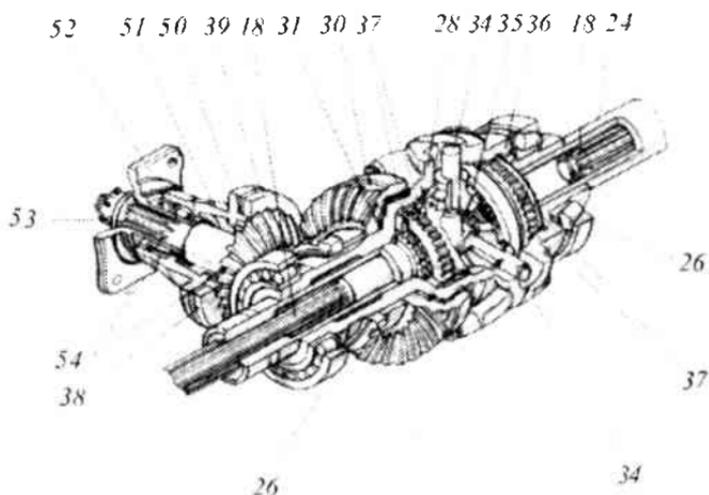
Дифференциал переднего ведущего моста трактора МТЗ-82 (см.рис. 4.4): 18 – полуоси; 24 – полуосевые шестерни; 26, 54 – подшипники; 28 – корпус дифференциала; 30 и 39 – ведомая и ведущая конические шестерни; 31 – регулировочное кольцо; 34 – оси сателлитов; 35 – сателлит; 36 – крышка; 37 – фрикционные диски; 38 – корпус моста; 50, 52 – регулировочные кольца; 51 – стакан подшипника; 53 – фланец
